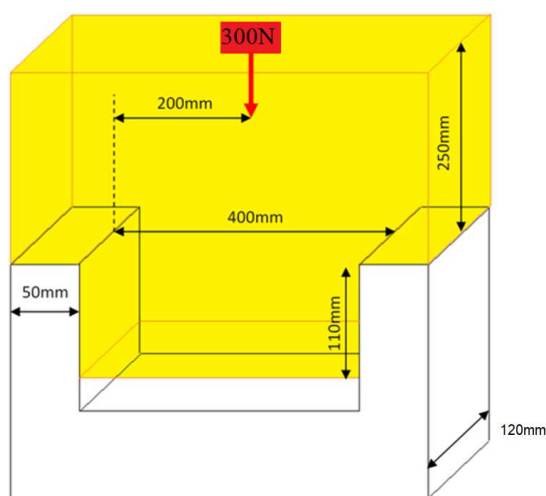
Modelo do suporte para ensaio e restrições de geometria da ponte.
